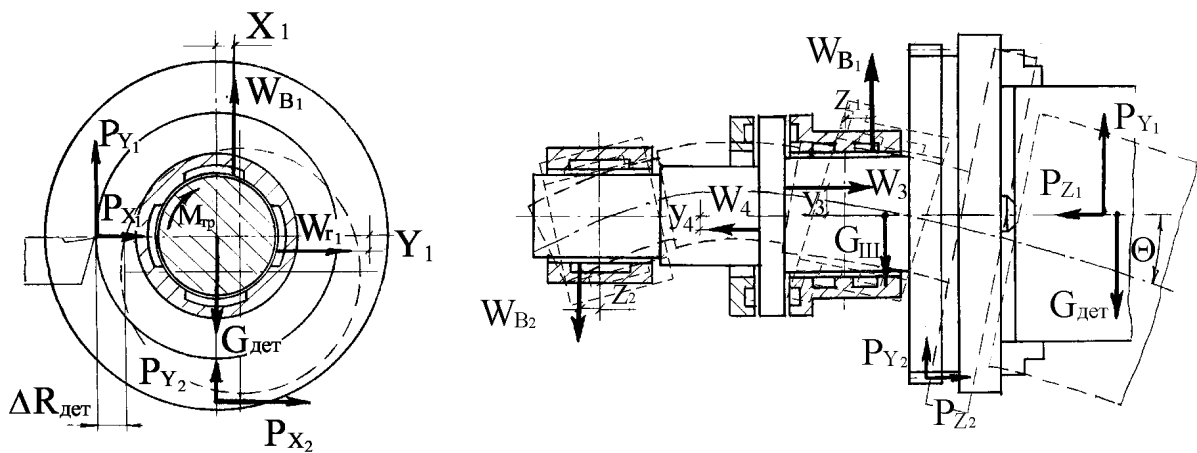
Розрахункова схема шпиндельного вузла важкого токарного верстата
